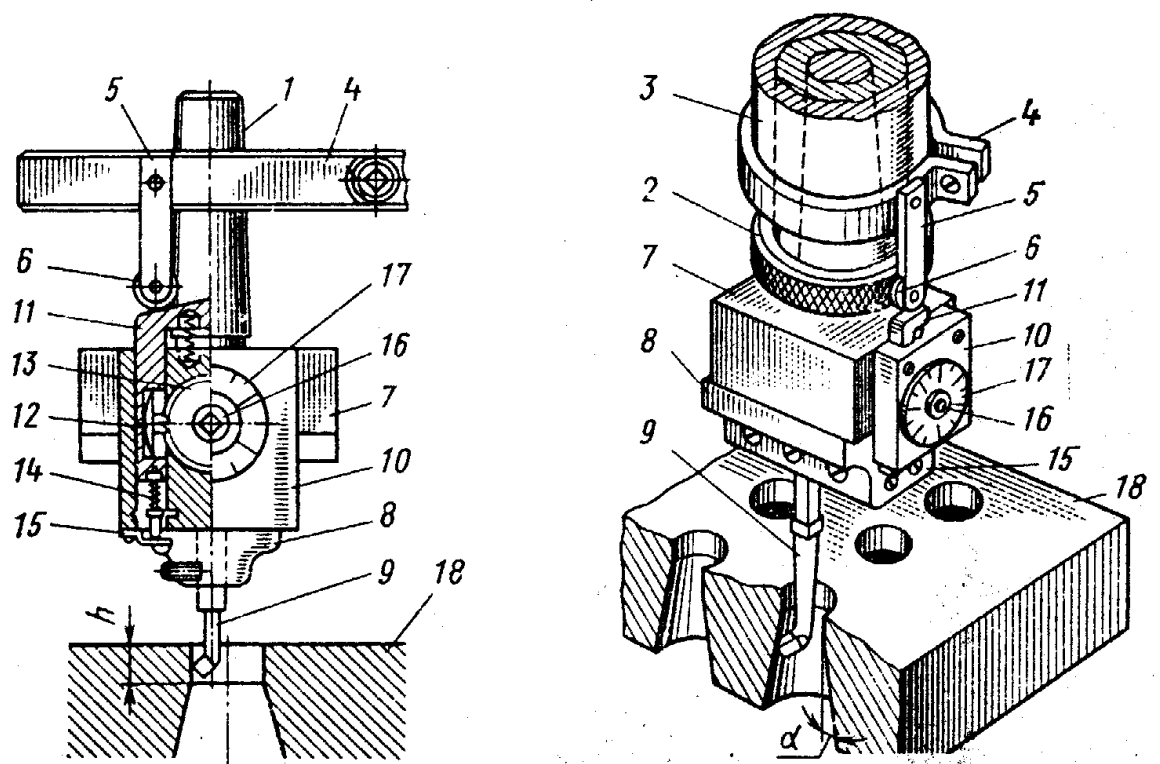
Универсальное приспособление для растачивания отверстий в матрицах штампов
